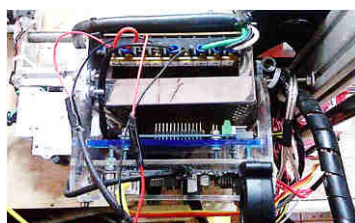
Montaje de la caja electrónica y enrutamiento de cables
